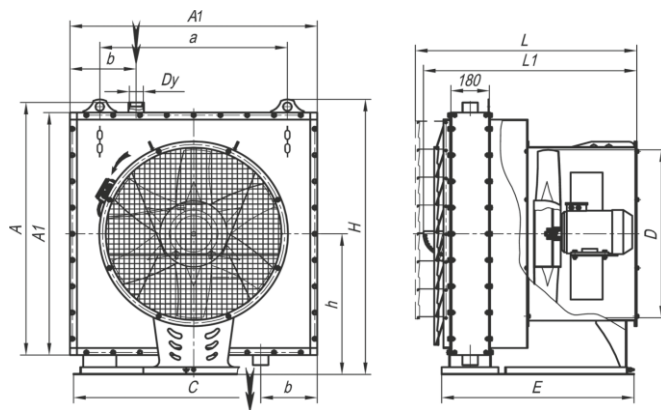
Габаритные и присоединительные размеры агрегатов АО 3-6,3П на базе воздухонагревателя типа КП.
